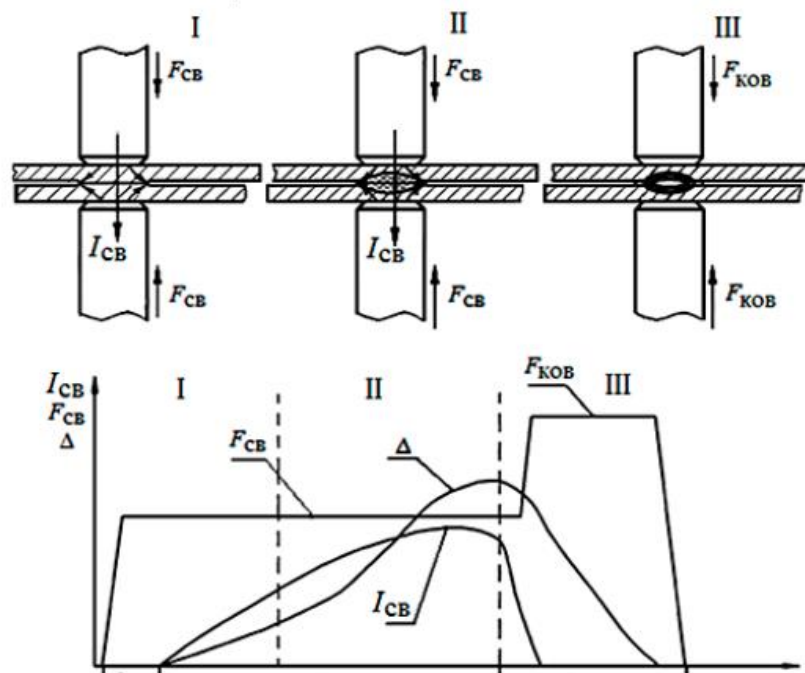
Етапи утворення з'єднання при точковому зварюванні
